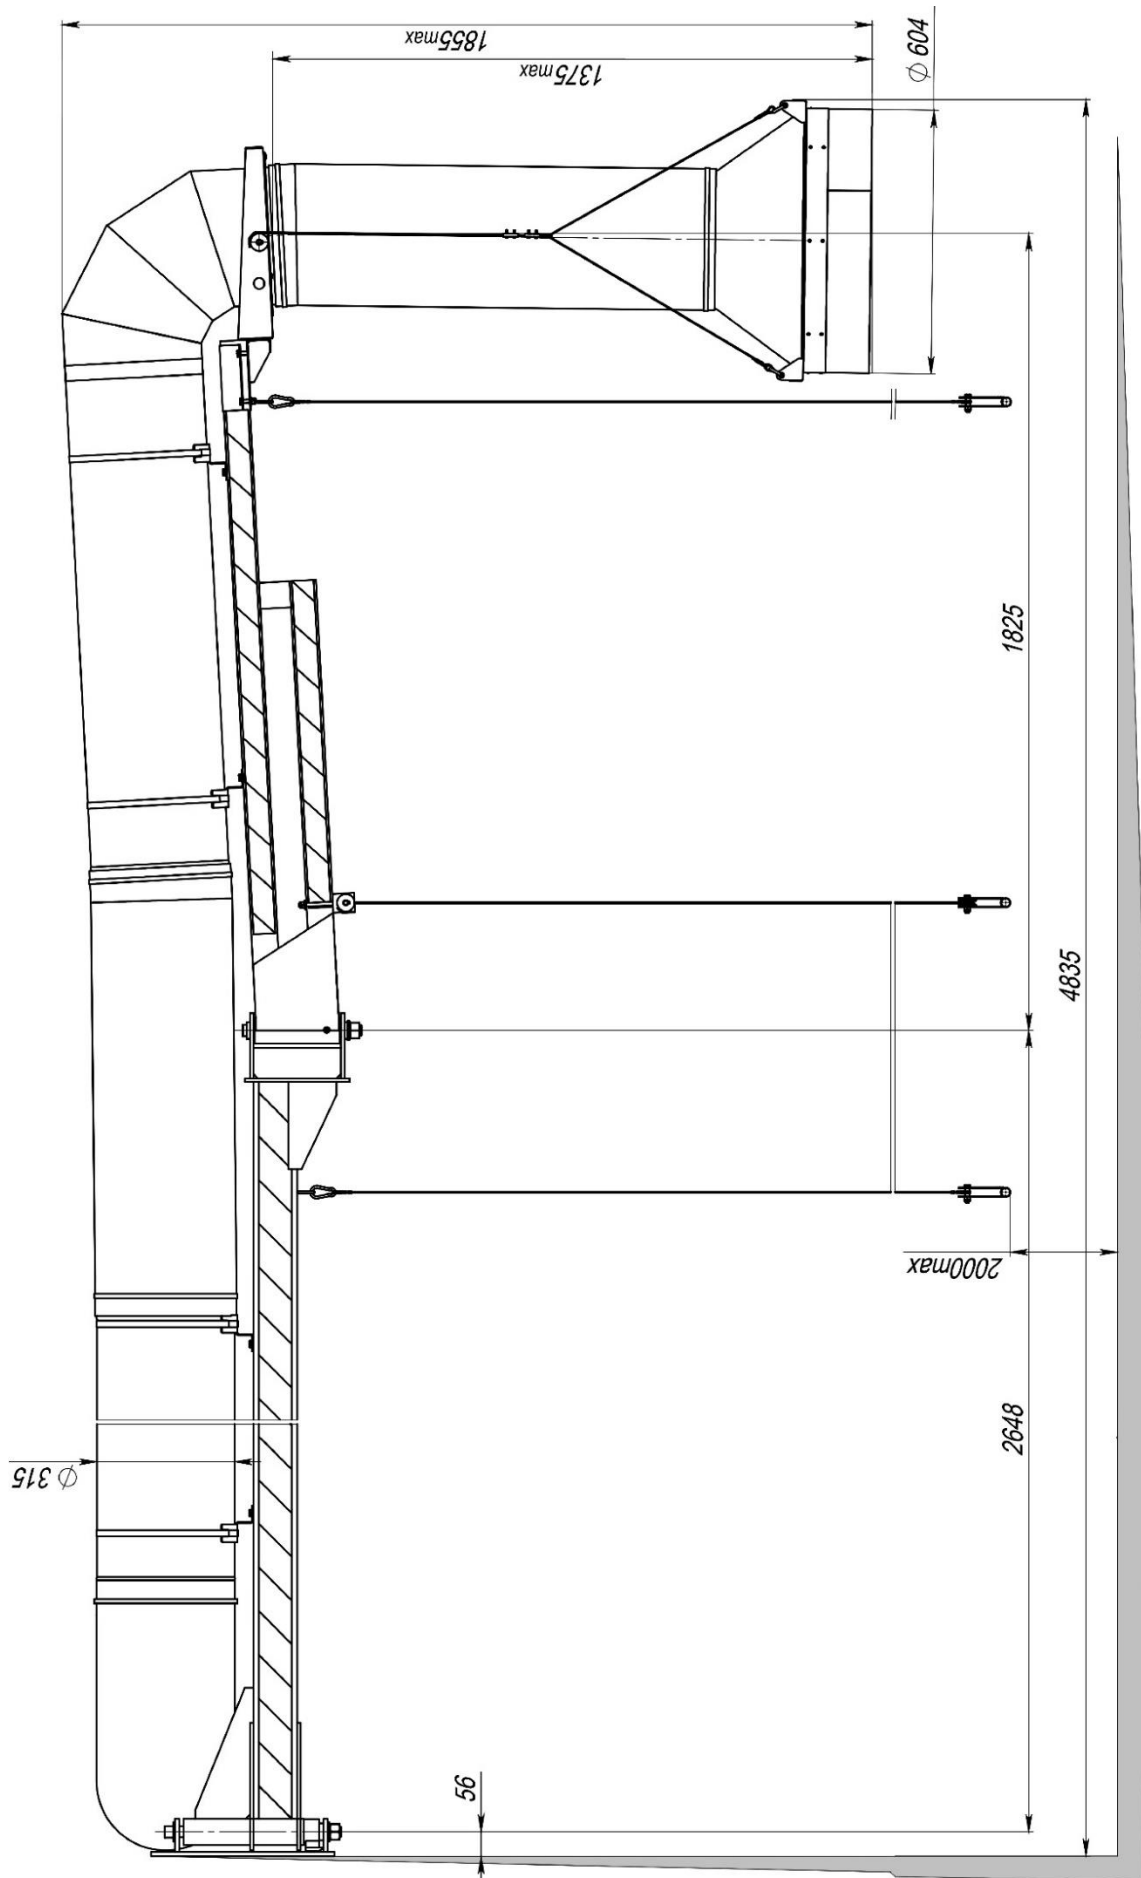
Габаритные размеры устройства УКЛ-4,5
